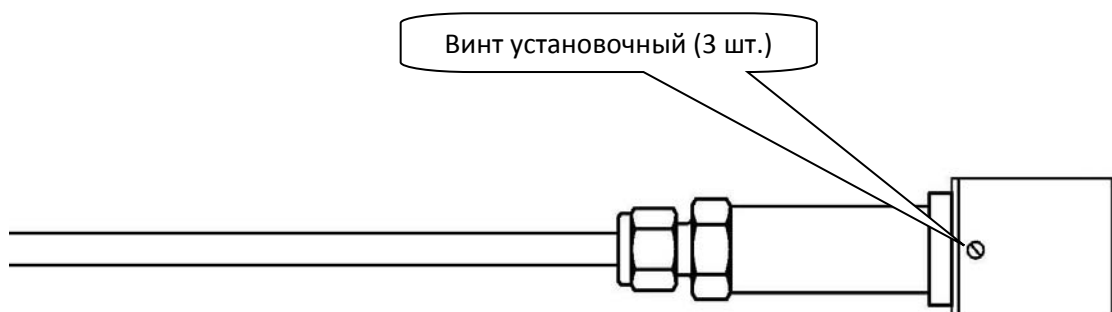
Расположение винта установочного на крышке корпуса уровнемера
